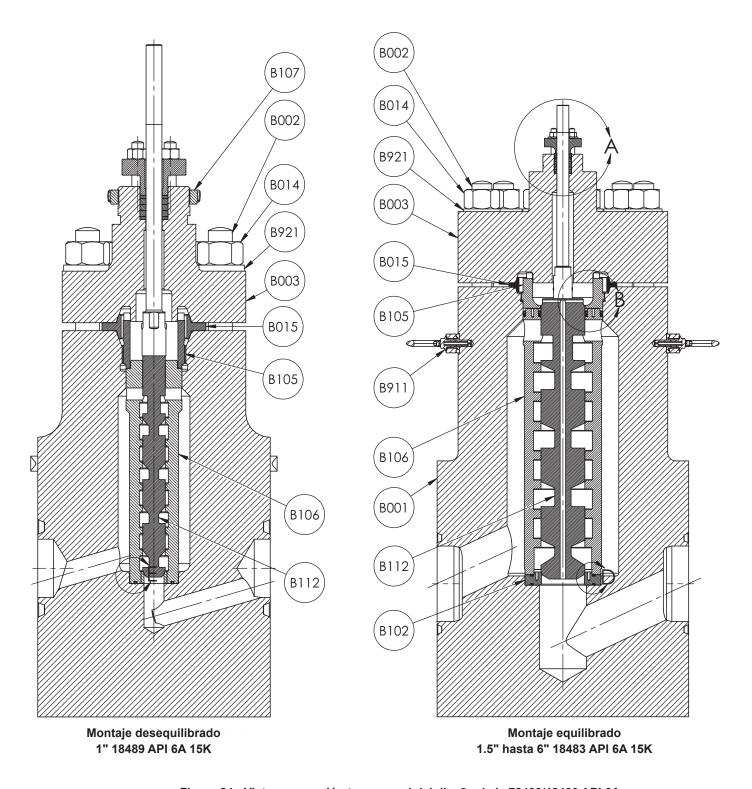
Vistas en sección transversal del diseño de la 78400/18400 API 6A
